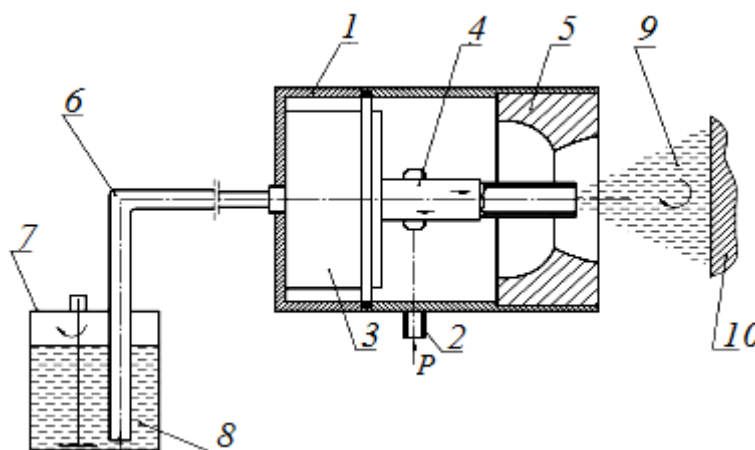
Схема обработки поверхностей изделий аэрозольным потоком
